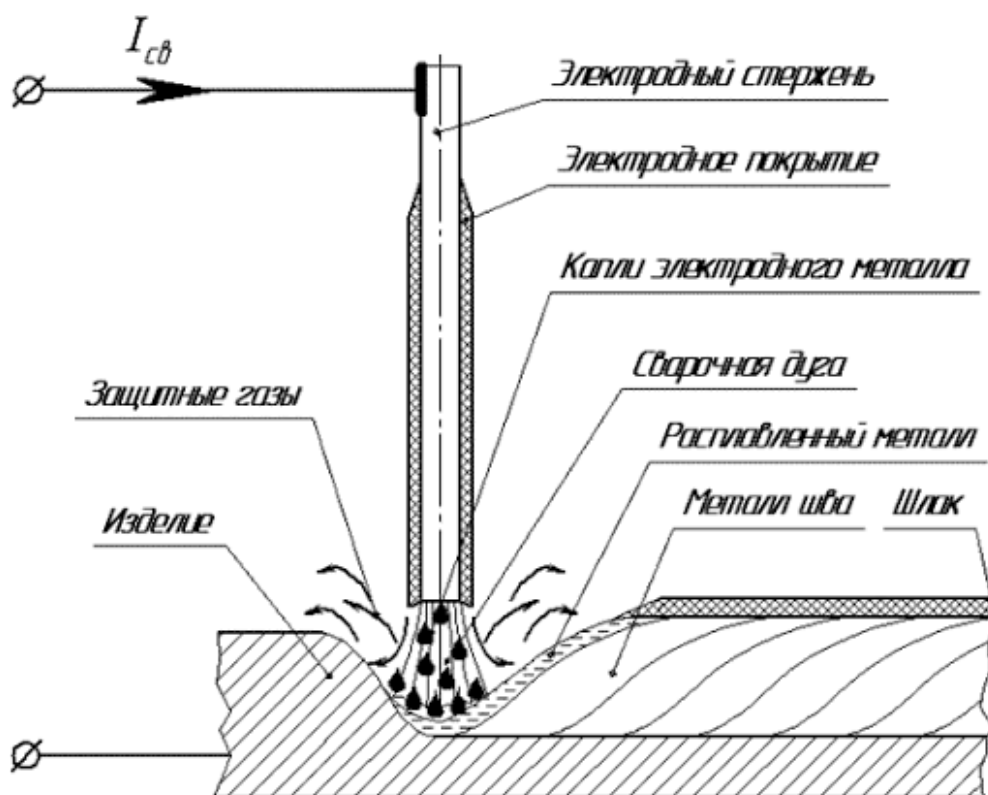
Схема сварки покрытыми электродами
